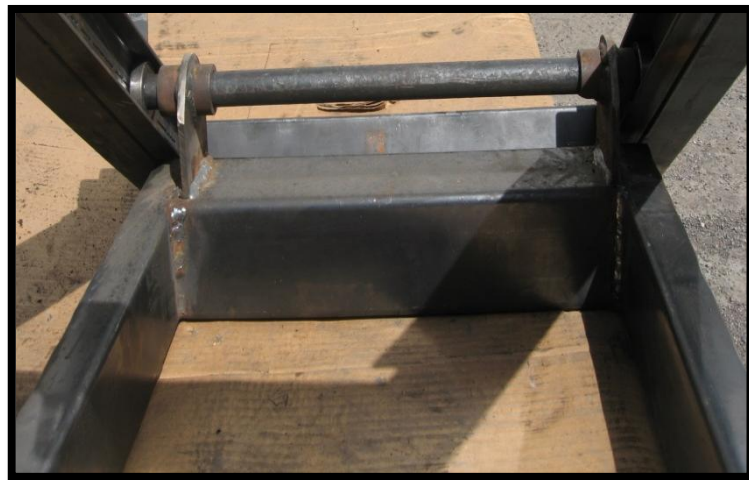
Soldadura de orejas de mesa deslizante .
